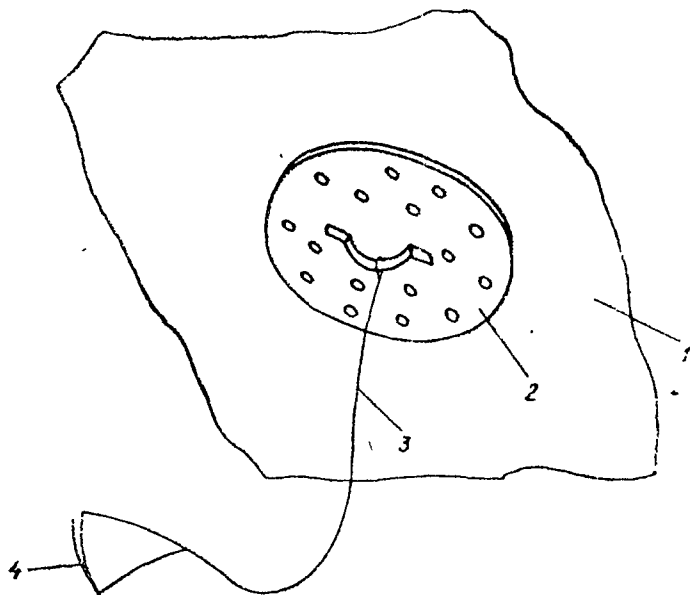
Приспособление для вытяжки вмятин на воздухозаборнике:
